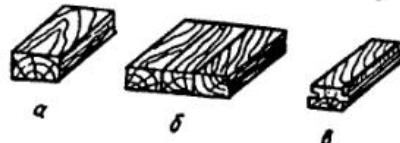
Заготовки: а — пиленные; б — клеенные; в — фрезерованные.
